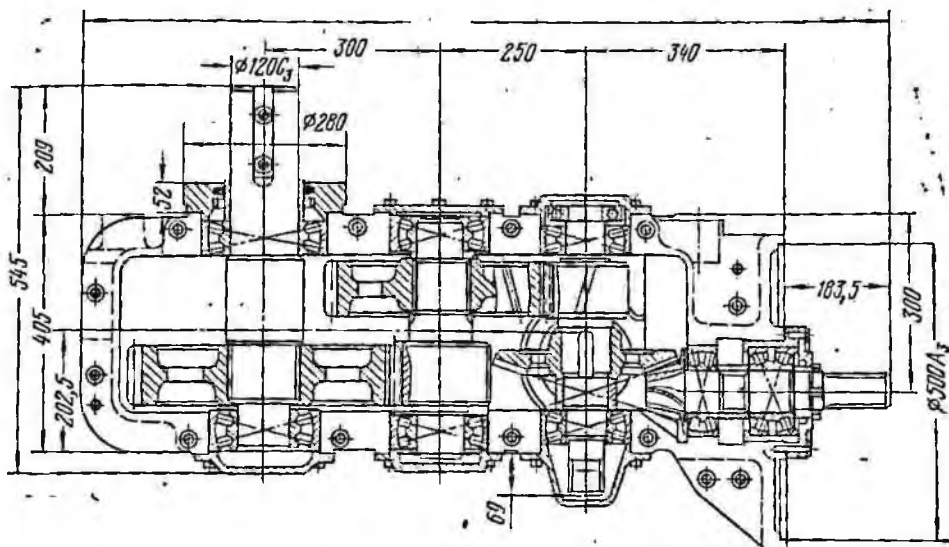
Редуктор трехступенчатый привода Т12-1АУ
